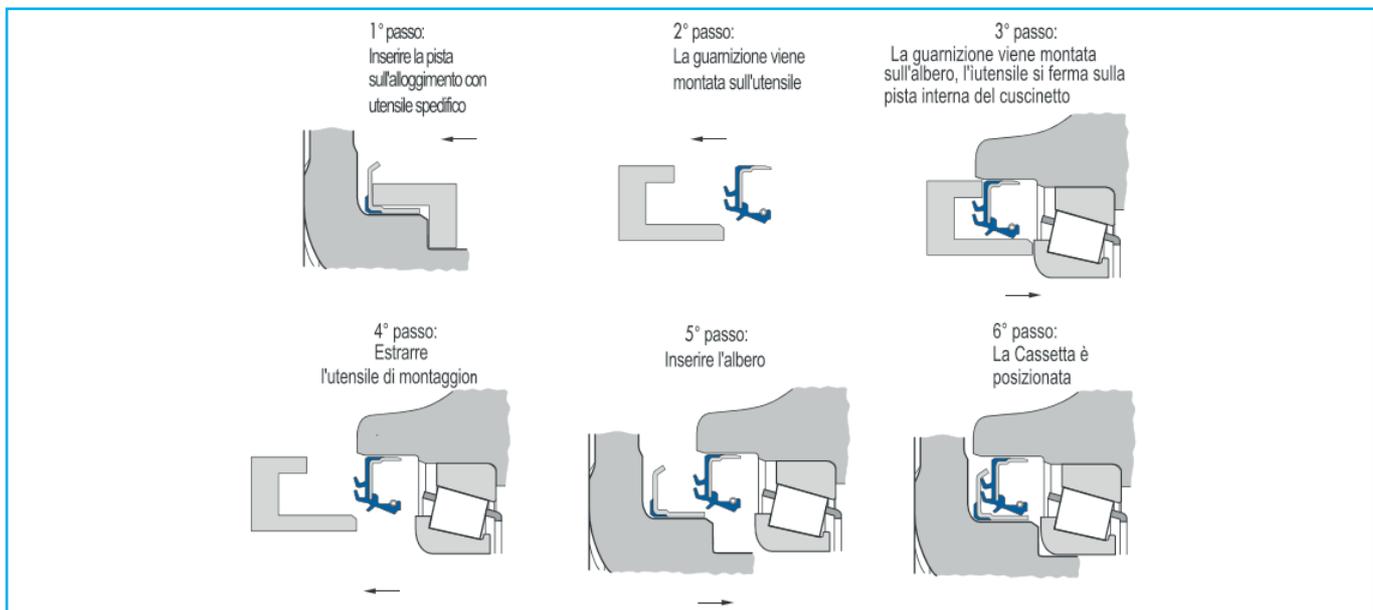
INSTALLAZIONE CASO E ("ASSEMBLAGGIO IN DUE FASI")
